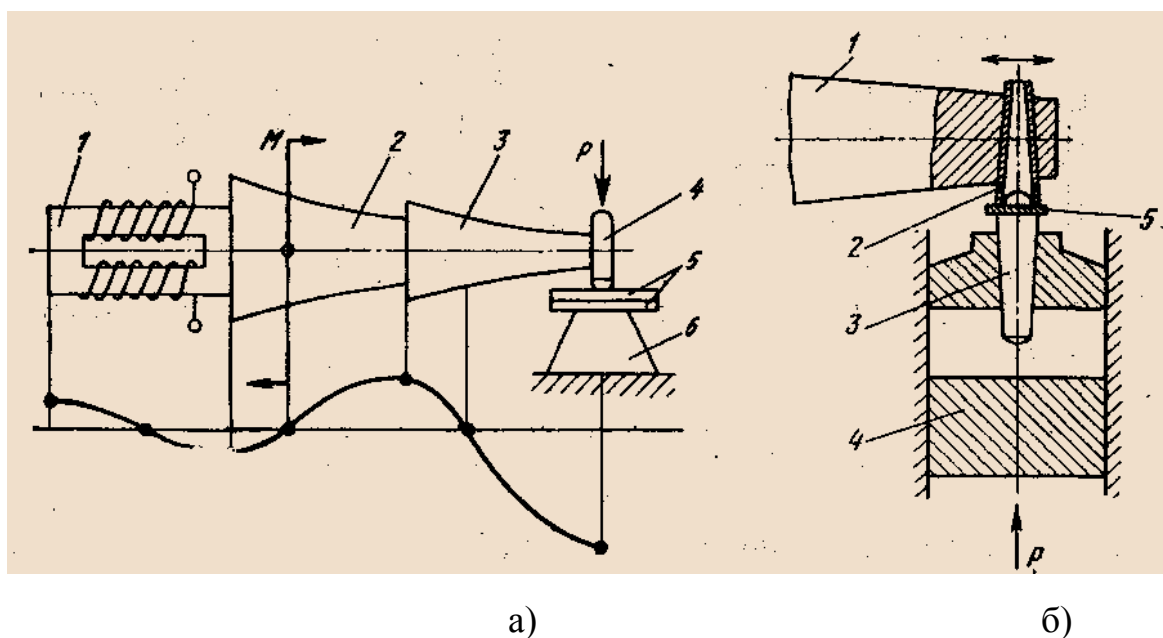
а – схема ультразвуковой сварки, где:
